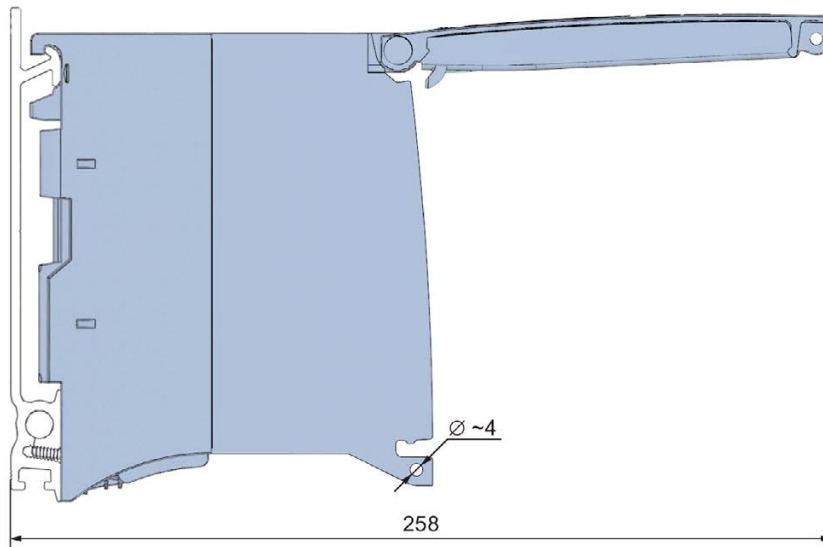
Maßbild CPU 1516-3 PN/DP, Seitenansicht mit geöffneter Frontklappe
